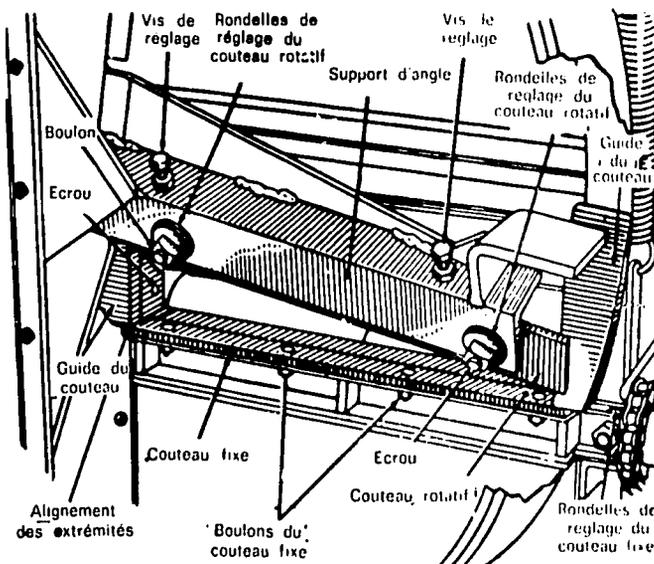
Dispositifs de réglage des couteaux sur un hache-paille
